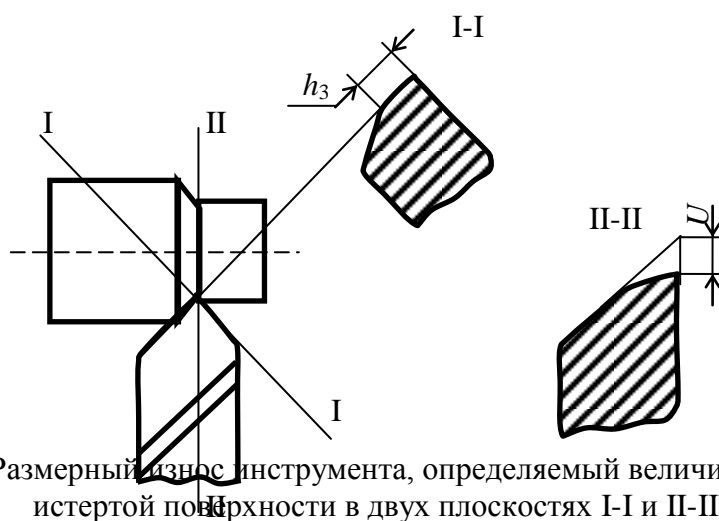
Размерный износ инструмента, определяемый величинами h_3 и U истертой поверхности в двух плоскостях I-I и II-II
